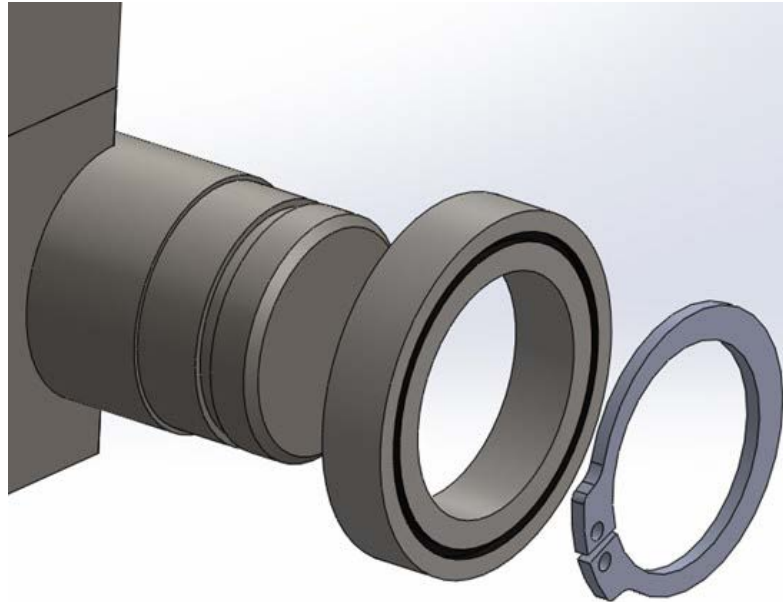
Desmontaje para los rodamientos en la plataforma.
